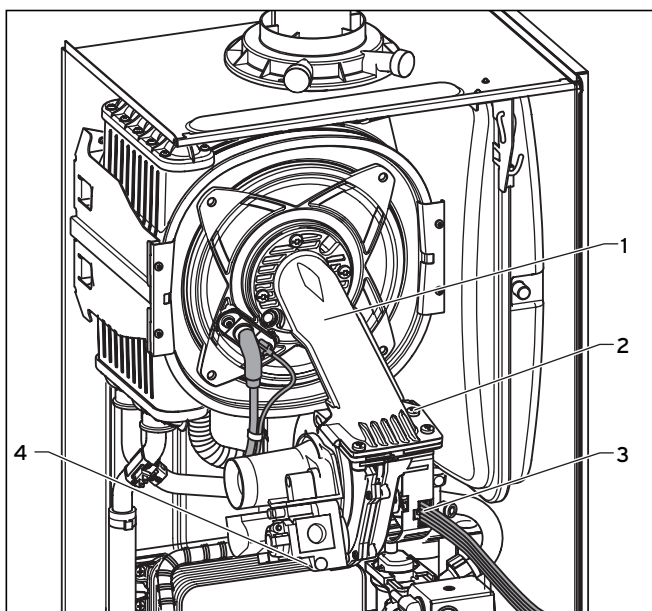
Демонтаж вентилятора с газовой арматурой
